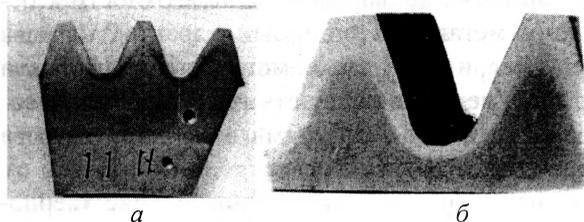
Макрошлифы шестерен из стали ПП закаленных по методу ОПЗ: а — цилиндрическая прямозубая шестерня автомобиля МАЗ, модуль  $m=6,25$ , сталь НИПРО, нагрев поверхностный индукционный; б — коническая шестерня с круговым зубом главной передачи автомобиля МАЗ, с внешним окружным модулем  $m=16$ , сталь У8А, нагрев объёмный печной
